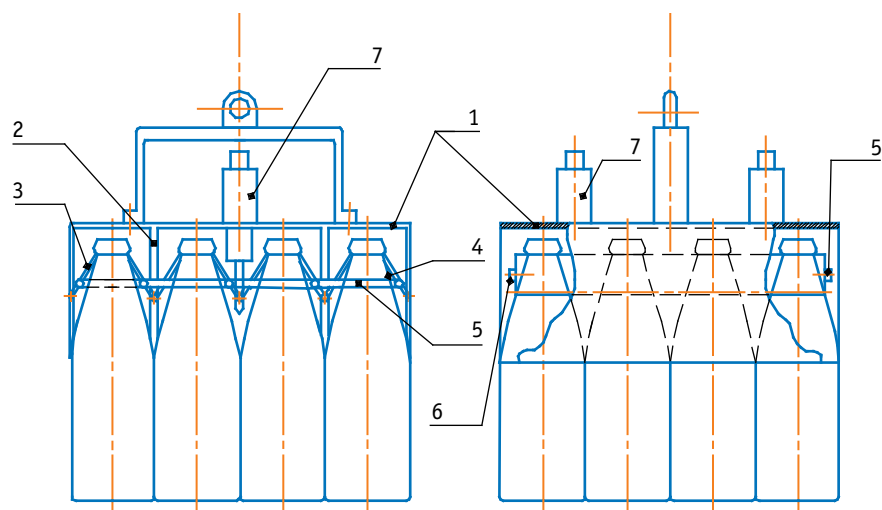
Захватна головка з рядними ЗП: 1 — корпус; 2 — міжрядні перегородки; 3, 4 — поворотні стулки; 5, 6 — цоки керування розкриттям поворотних стулок; 7 — пневмоциліндри
